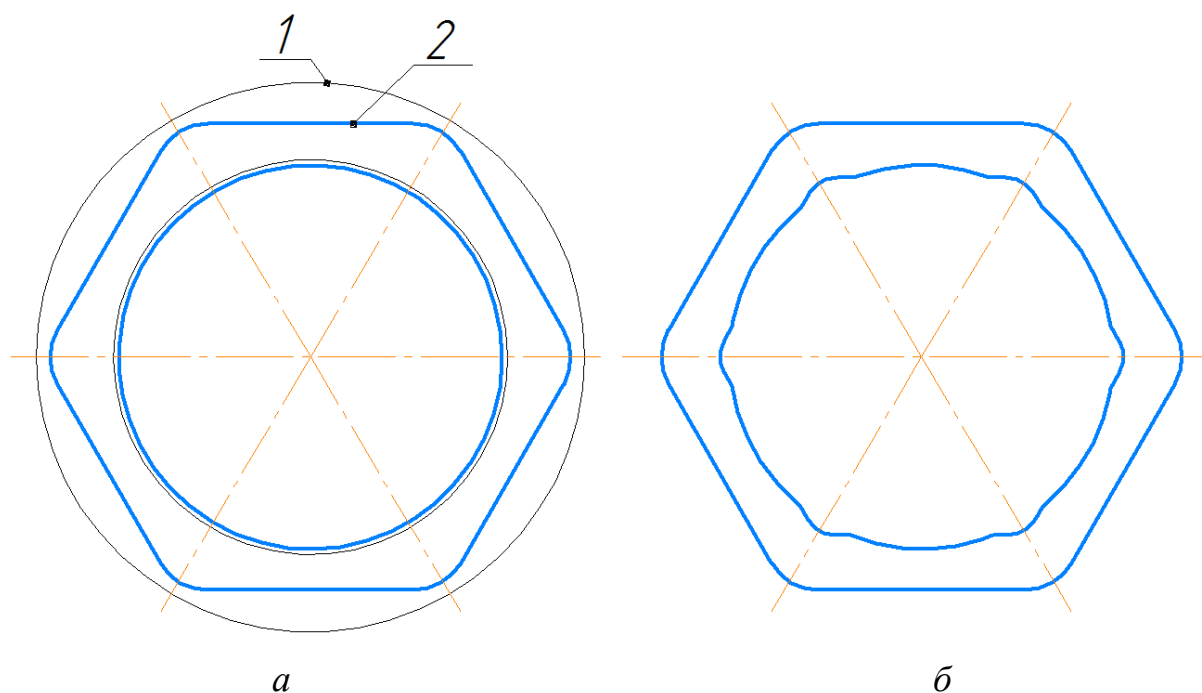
Влияние размеров заготовки на геометрию готовой трубы: а – поперечное сечение при правильном выборе заготовки (1 – заготовка, 2 – готовая труба), б – поперечное сечение при уменьшенной толщине стенки.
